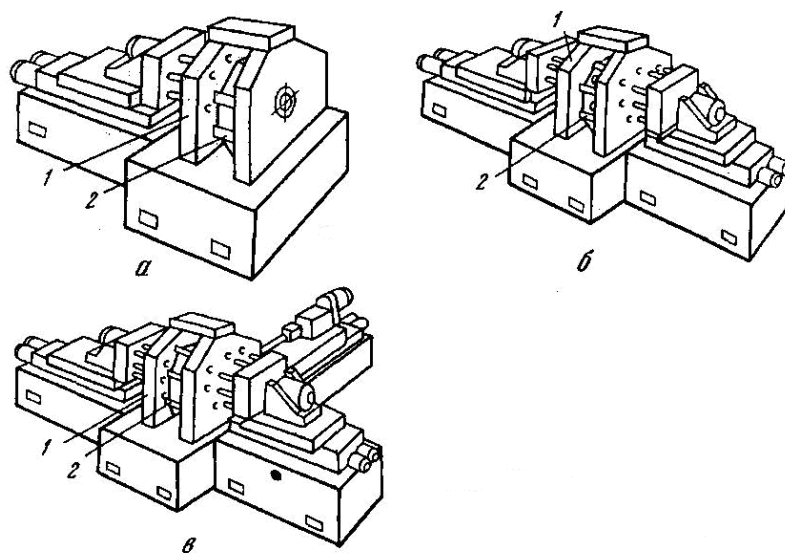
Типові компоновки агрегатних верстатів з поворотним ділильним барабаном
